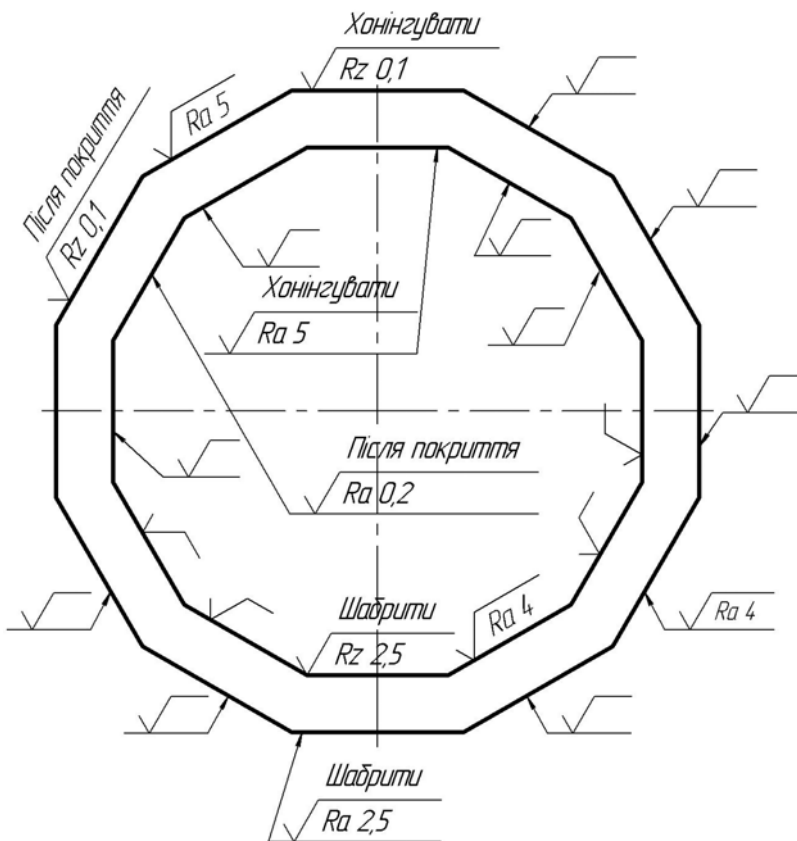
Розташування знаків шорсткості на кресленниках
